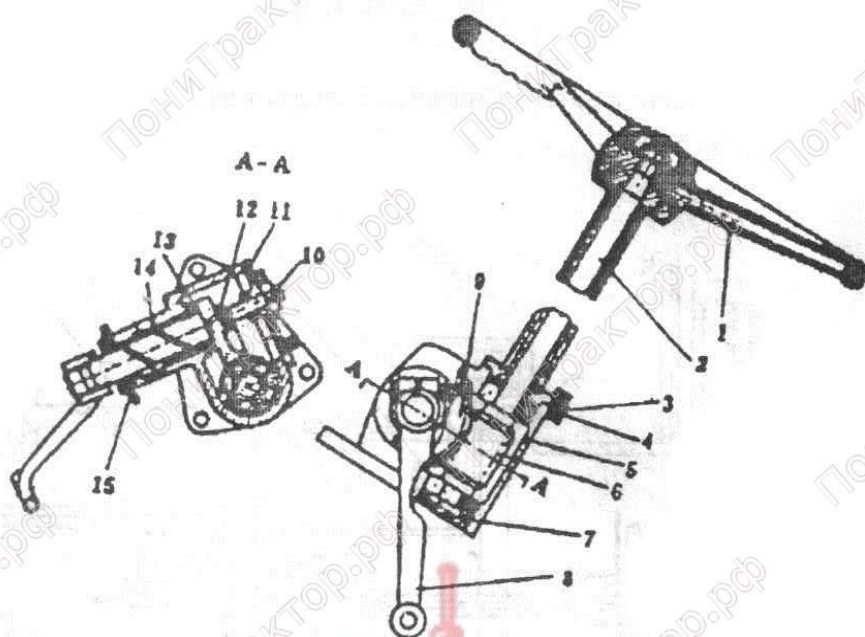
Рулевое управление: 1-колесо рулевого управления; 2-вал рулевого управления 3- крышка верхняя; 4-прокладка; 5-картер рулевого управления; 6-червяк поворотный; 7-крышка нижняя; 8-сошка рулевого управления; 9-червячный сектор; 10-болт крепления; 11- крышка боковая; 12-прокладка стопорная; 13-прокладки регулировочные; 14-втулка регулирующего сердечника; 15-крышка пылезащитная
